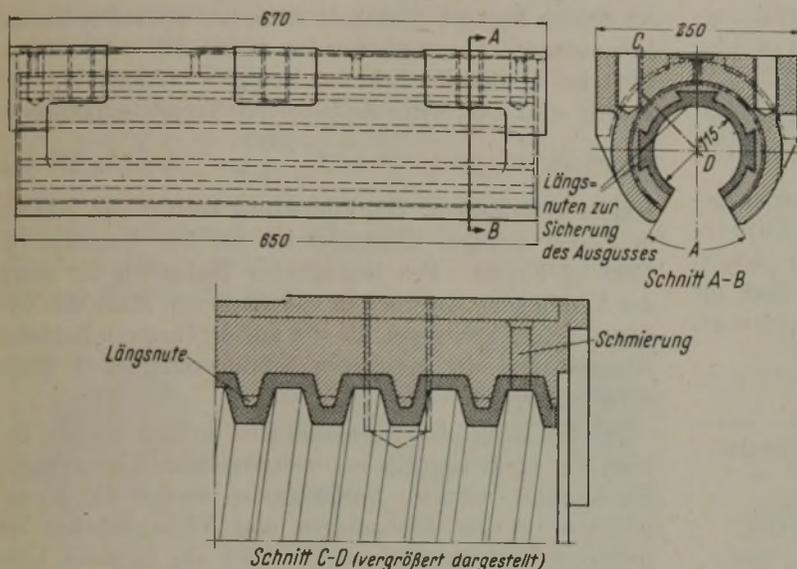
Spindelmutter für Blechkantenhobelmachine. Rechtes Leitspindelgewinde, 2fach, 3'' Steigung (76,2 mm).
